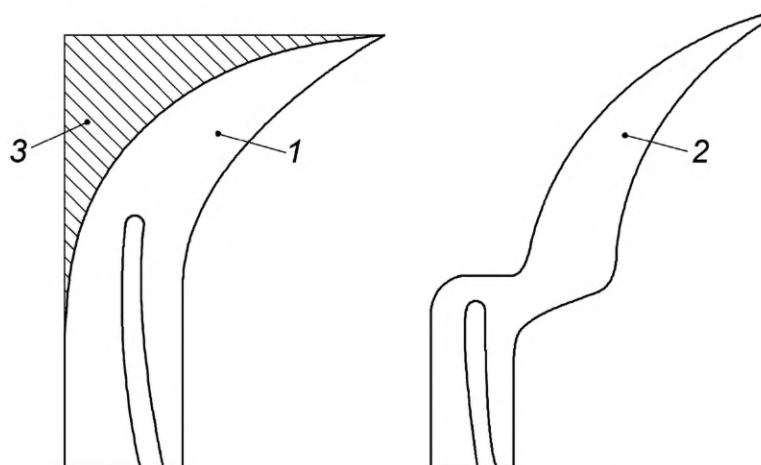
Расположение зазоров для расклинивающего ножа
